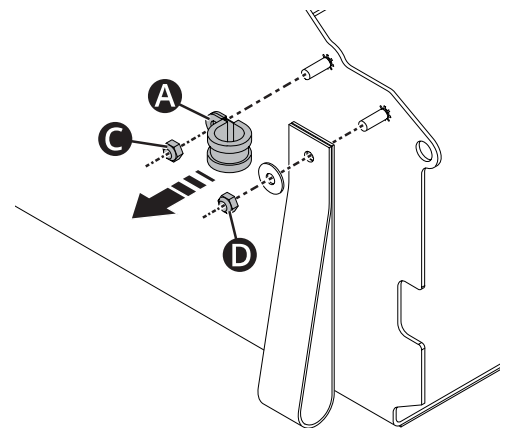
Mutter C und Kabelring A entfernen und Mutter D lösen.
